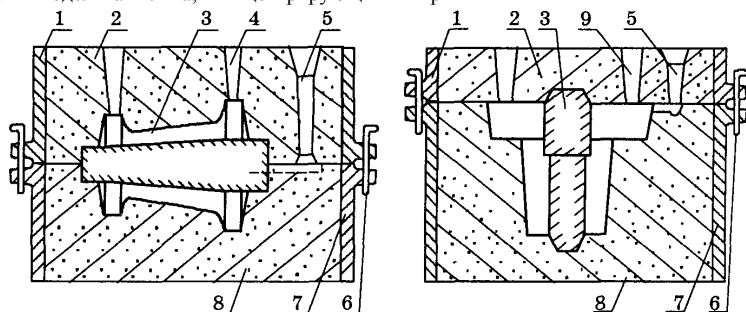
Эскизы литейных форм в сборке: 1 — верхняя опока;
